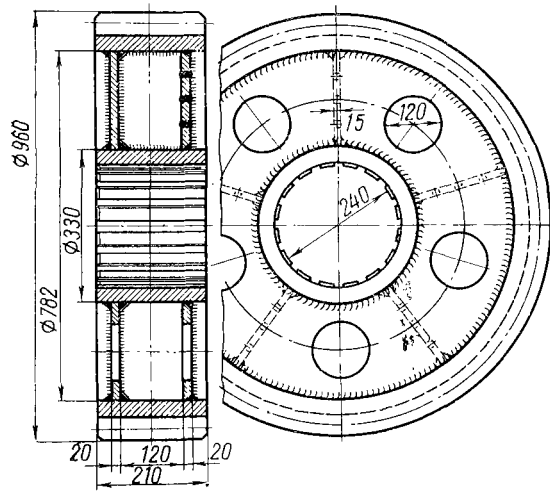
Двустенчатое сварное зубчатое колесо
